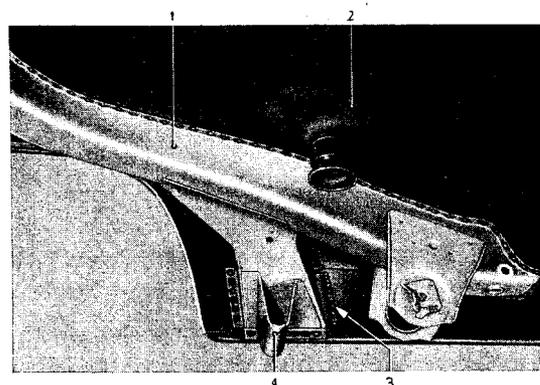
Vorderer senkrechter Flansch des Längsträgerzwischenstückes lichtbogenschweißt
